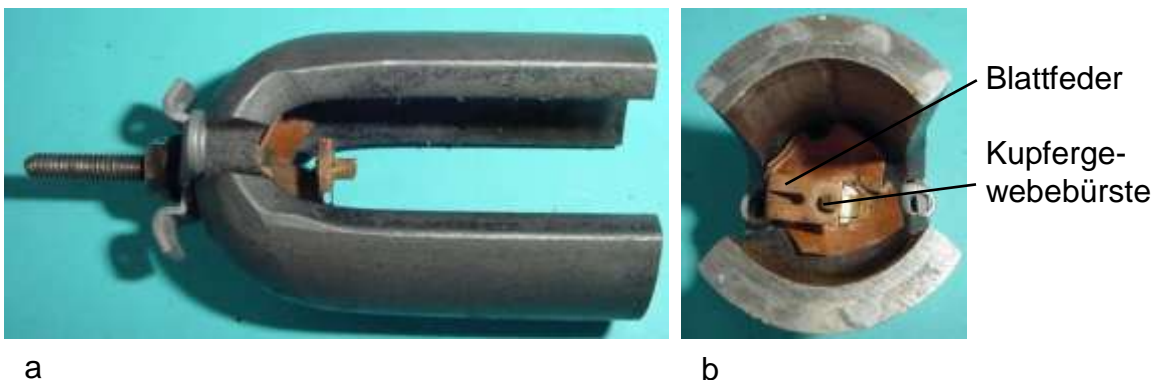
Stromleitung durch den Magneten: a) Seitenansicht des Kabelanschlussbol- zens, b) Kontaktfeder über dem Magnetjoch
